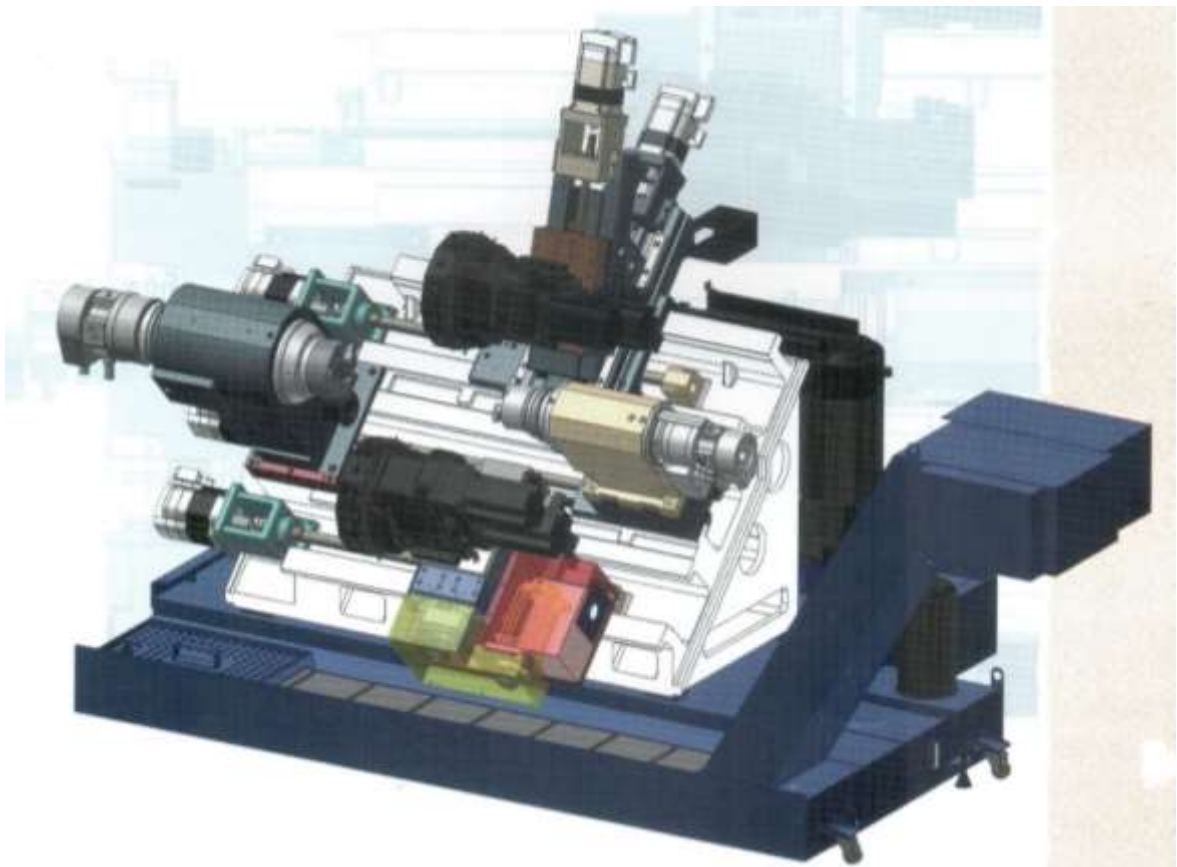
Двошпindelний верстат мод. ТТС 300
